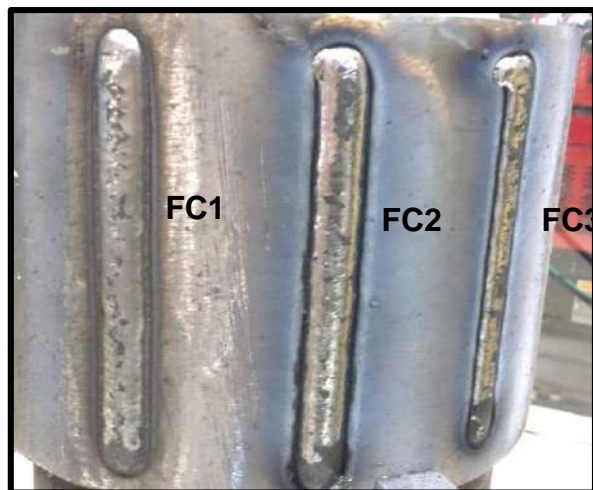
Cordões de simples deposição soldados por processo FCAW.
